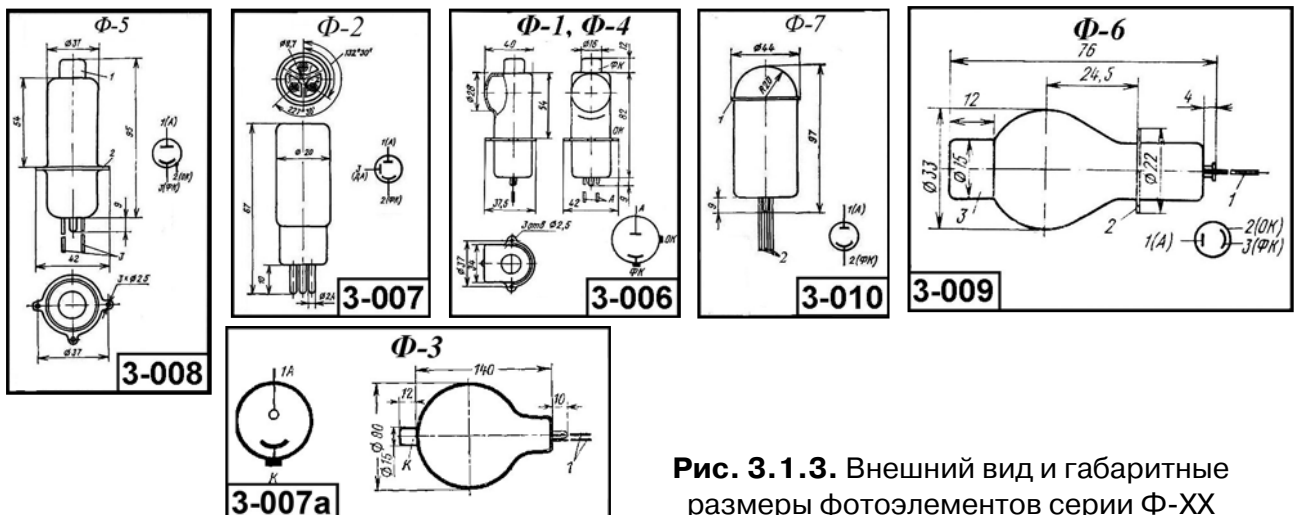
Внешний вид и габаритные размеры фотоэлементов серии Ф-XX
